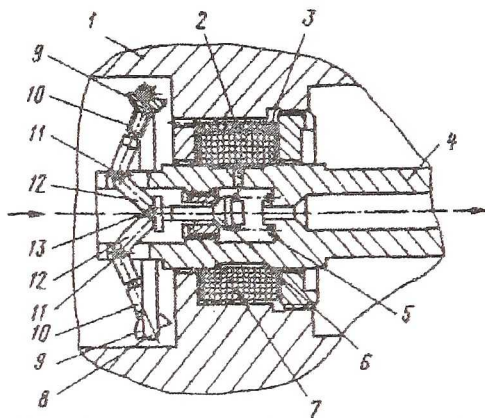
Опора ротора с подводом смазки: 1 - корпус; 2 - металлорезиновая прокладка; 3 - полимерное покрытие; 4 - ротор; 5 - пружина; 6 - клапан (золотник); 7 - седло; 8 - браслетная пружина; 9 - сосредоточенная масса; 10, 12 - плечи рычага; 11 - шарнир; 13 - толкатель
